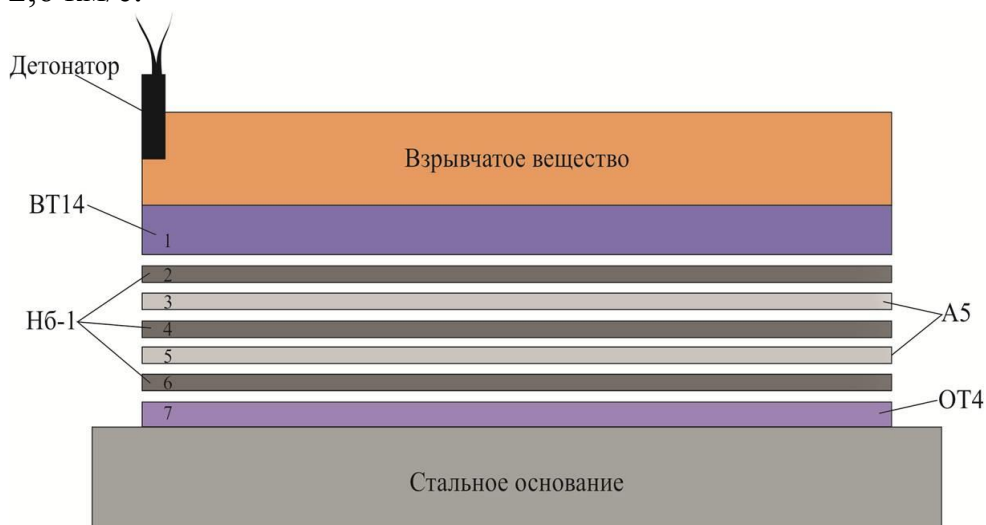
Схема сварки взрывом многослойного композита Nb и Al
